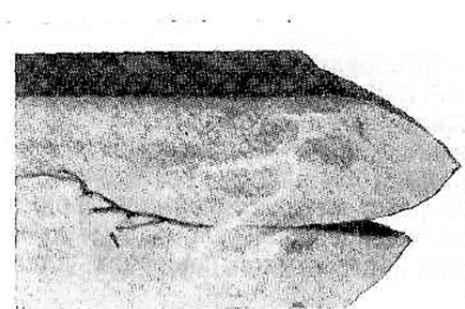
Торець заготовки після прокатки на блюмінгу [28]
